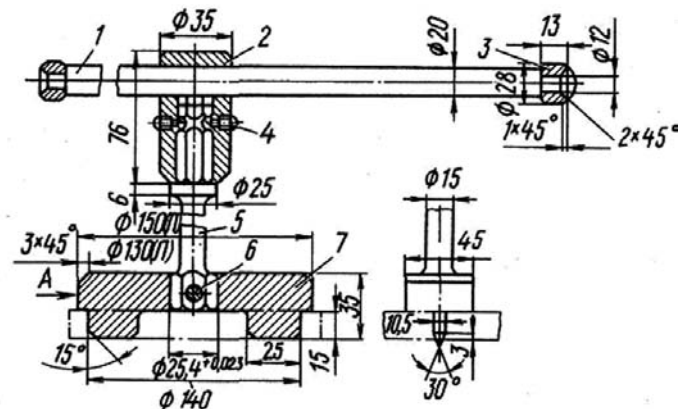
Ключ для регулировочных гаек правого и левого подшипников дифференциала: 1 — рукоятка; 2 — корпус; 3 — кольцо; 4 — винт; 5 — вставка; 6 — штифт; 7 — головка
